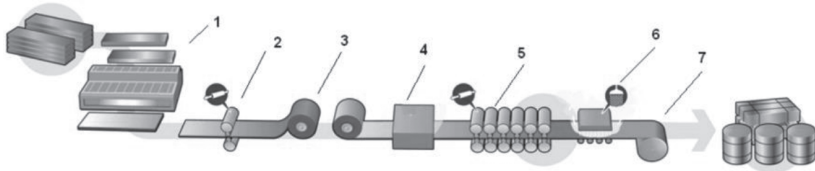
Розташування устаткування стана нескінченної прокатки штаб фірми Kawasaki Steel:
